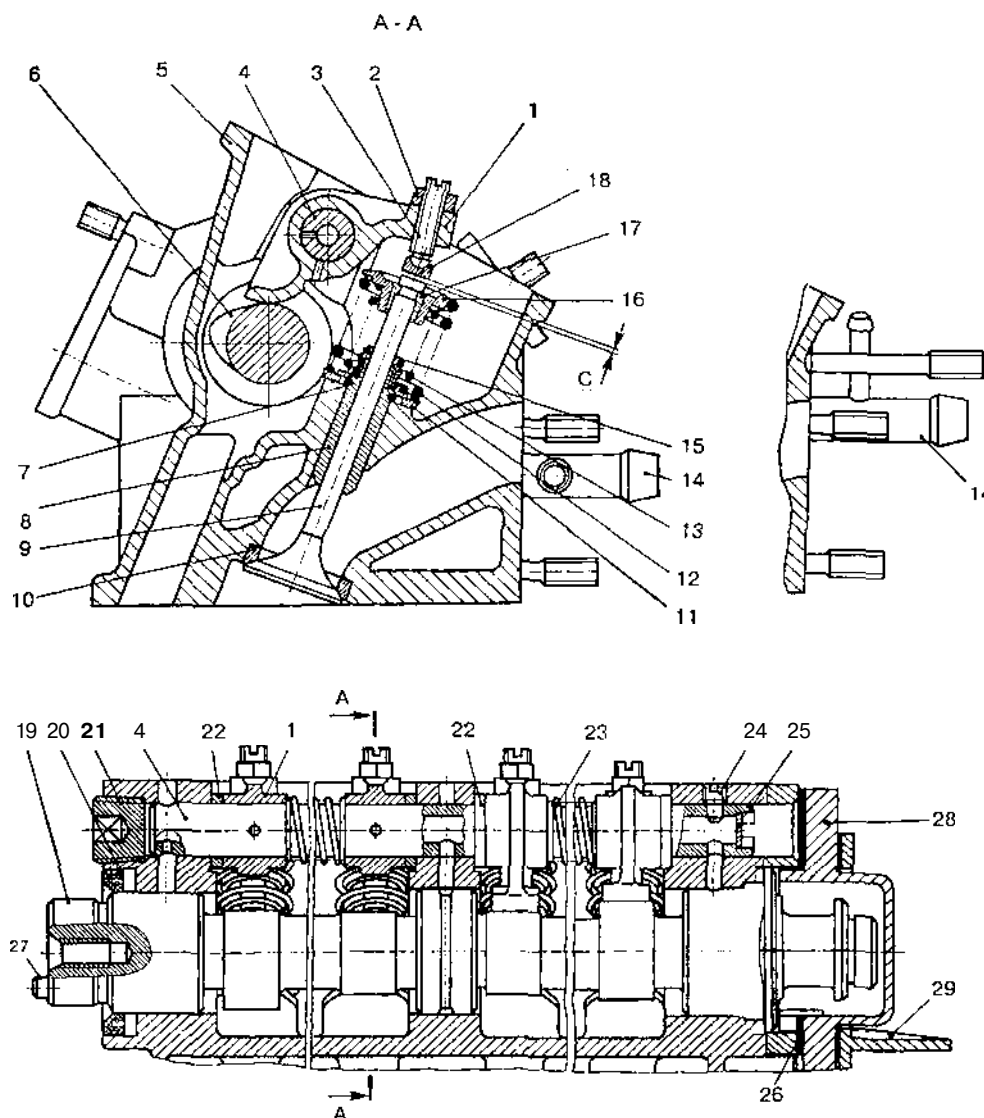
Головка цилиндров и схема регулировки зазоров в механизме привода клапанов:
